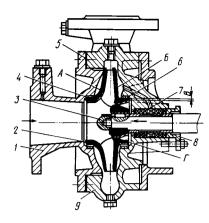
Центробежный насос типа K: I — крышка; 2 — рабочее колесо; 3 — гайка крепления рабочего колеса; 4, 6 — уплотнительные кольца; 5 — прокладка; 7 — набивка сальника; 8 — нажимная втулка сальника; 9 — корпус; A — передний диск; B — задний диск; B — радиальный зазор между уплотнительными поверхностями;  $\Gamma$  — разгрузочное отверстие
